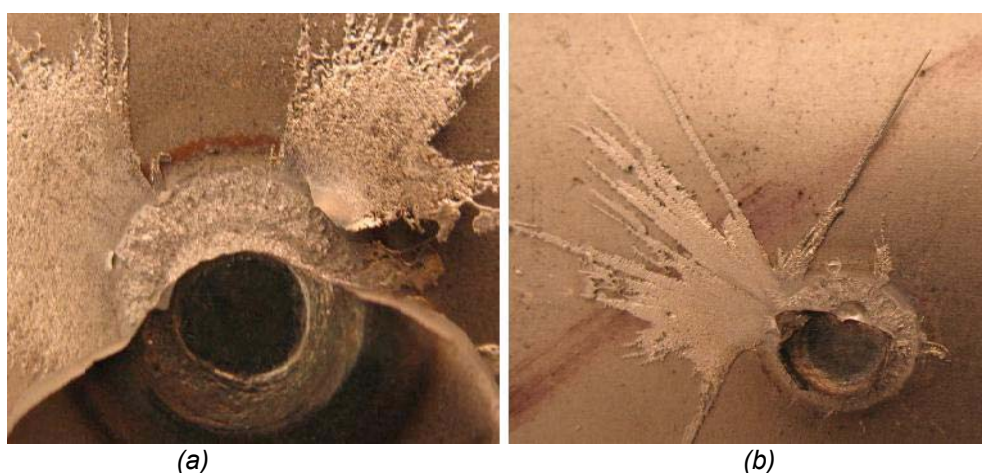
Aspecto da fratura dos botões de solda realizados após teste de arrancamento para o aço DP 800 não revestido. (a) Soldagem com 9 kA, 25 ciclos de corrente e 2,6 kN de força nos eletrodos e (b) Soldagem com 7 kA, 15 ciclos de corrente e 1,6 kN de força nos eletrodos.
